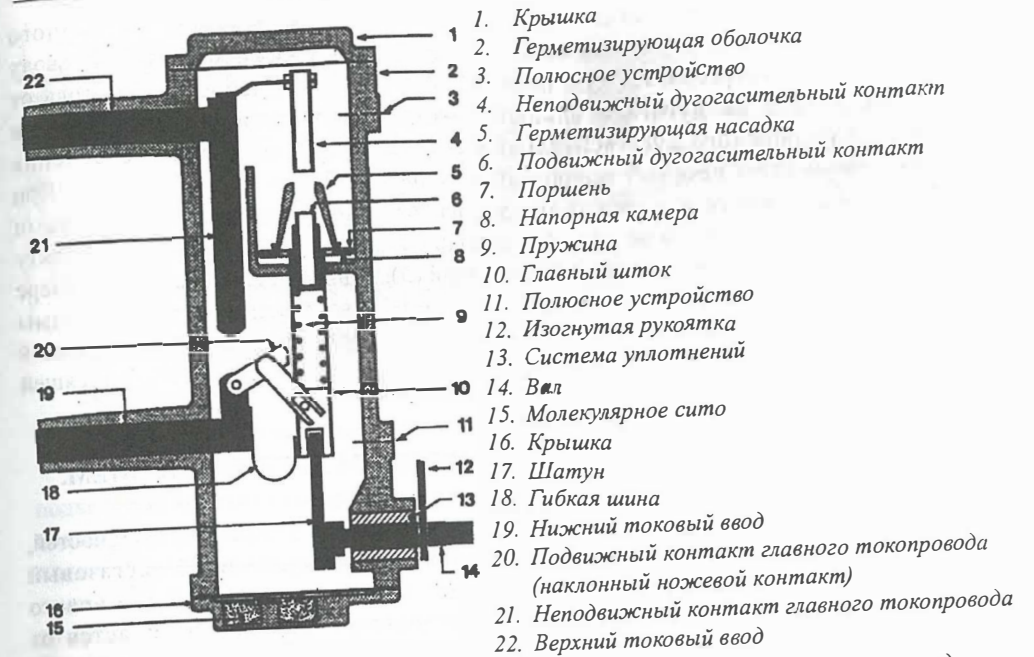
Автокомпрессионный элегазовый выключатель с главными токоведущими контактами
